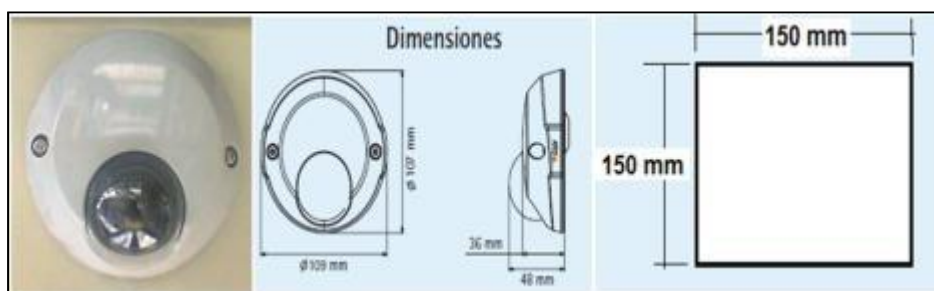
Detalle dimensiones de la platina de soporte para el contador de pasajeros
